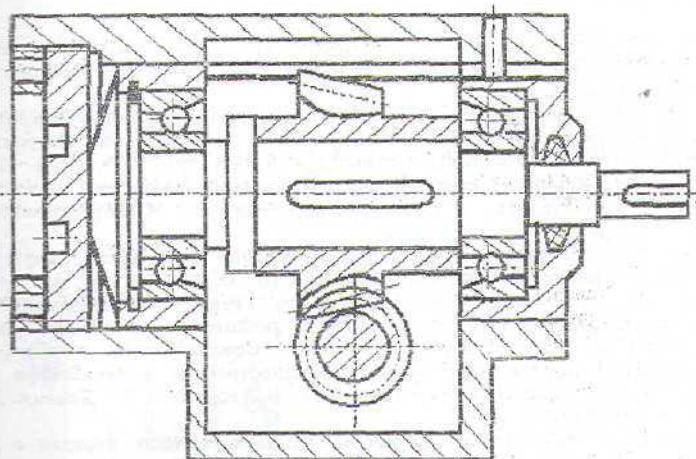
Конструкция редуктора перемещения пильного узла ленточной
